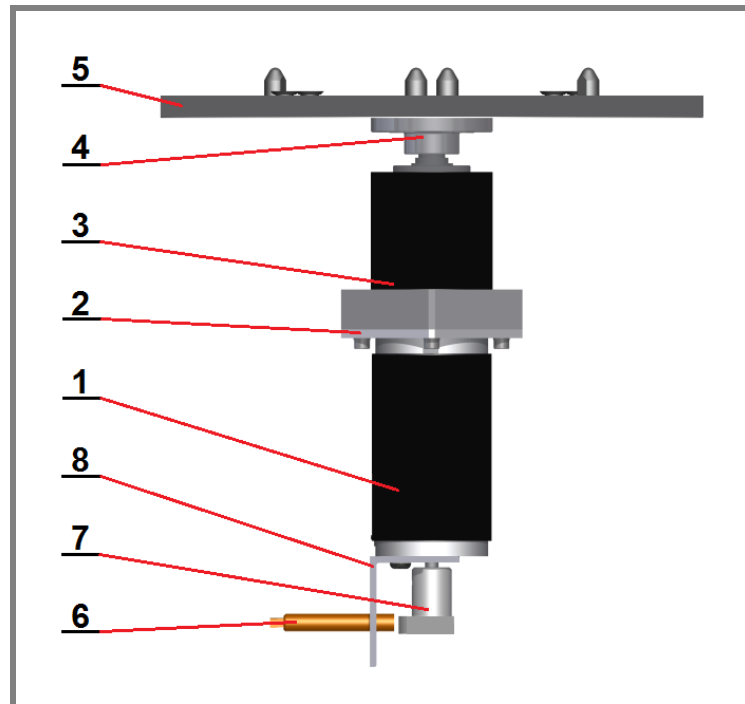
Komponenty ručního přísuvu stříkací pistole.
